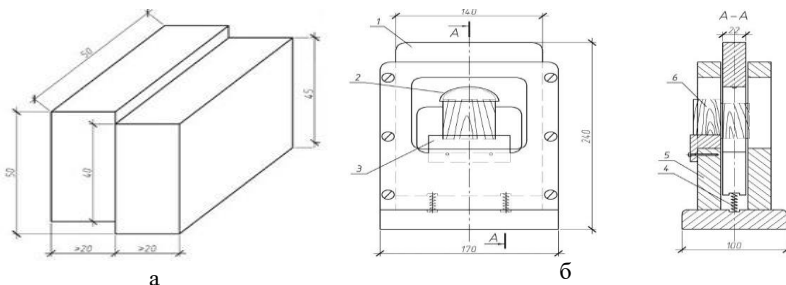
Визначення міцності клеєвого з'єднання на сколювання: а – форма та розміри зразка; б – приспособлення; 1 – пуансон; 2 – самоцентруюча опора; 3 – вкладка; 4 – пружина; 5 – стійка опори; 6 – зразок
